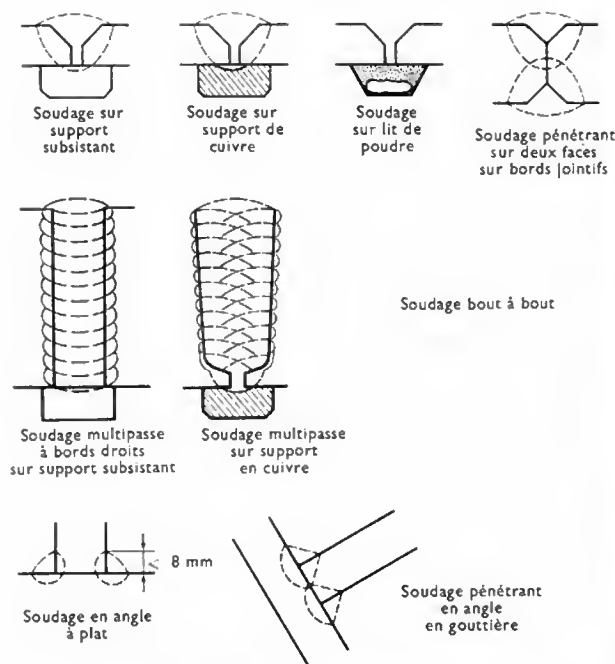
Préparations et formes de soudures à l'arc sous flux de poudre
